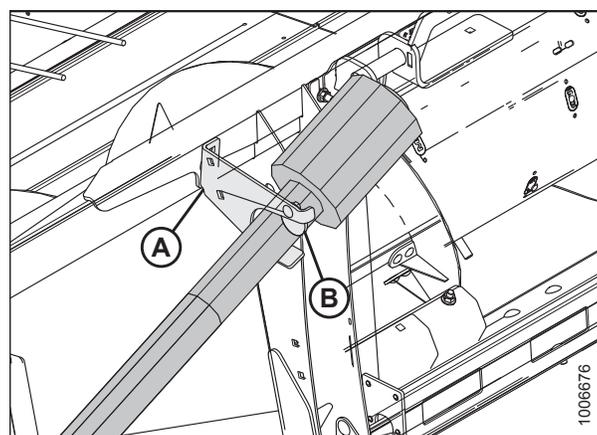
Extremo de la cosechadora del cardán en posición de almacenamiento
